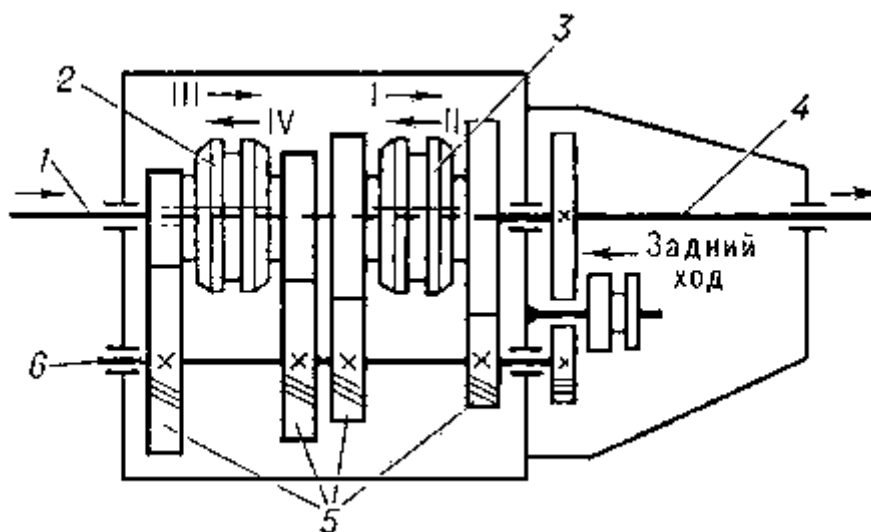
Схема механической автомобильной четырёхступенчатой (I—IV) коробки передач: 1 — первичный вал; 2, 3 — муфты с синхронизаторами; 4 — выходной вал; 5 — шестерни, входящие в зацепление с зубчатыми колёсами; 6 — вторичный вал
